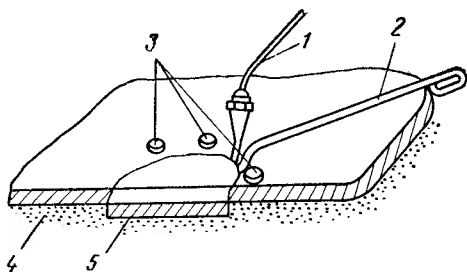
Схема сварки деталей из алюминиевых сплавов:
